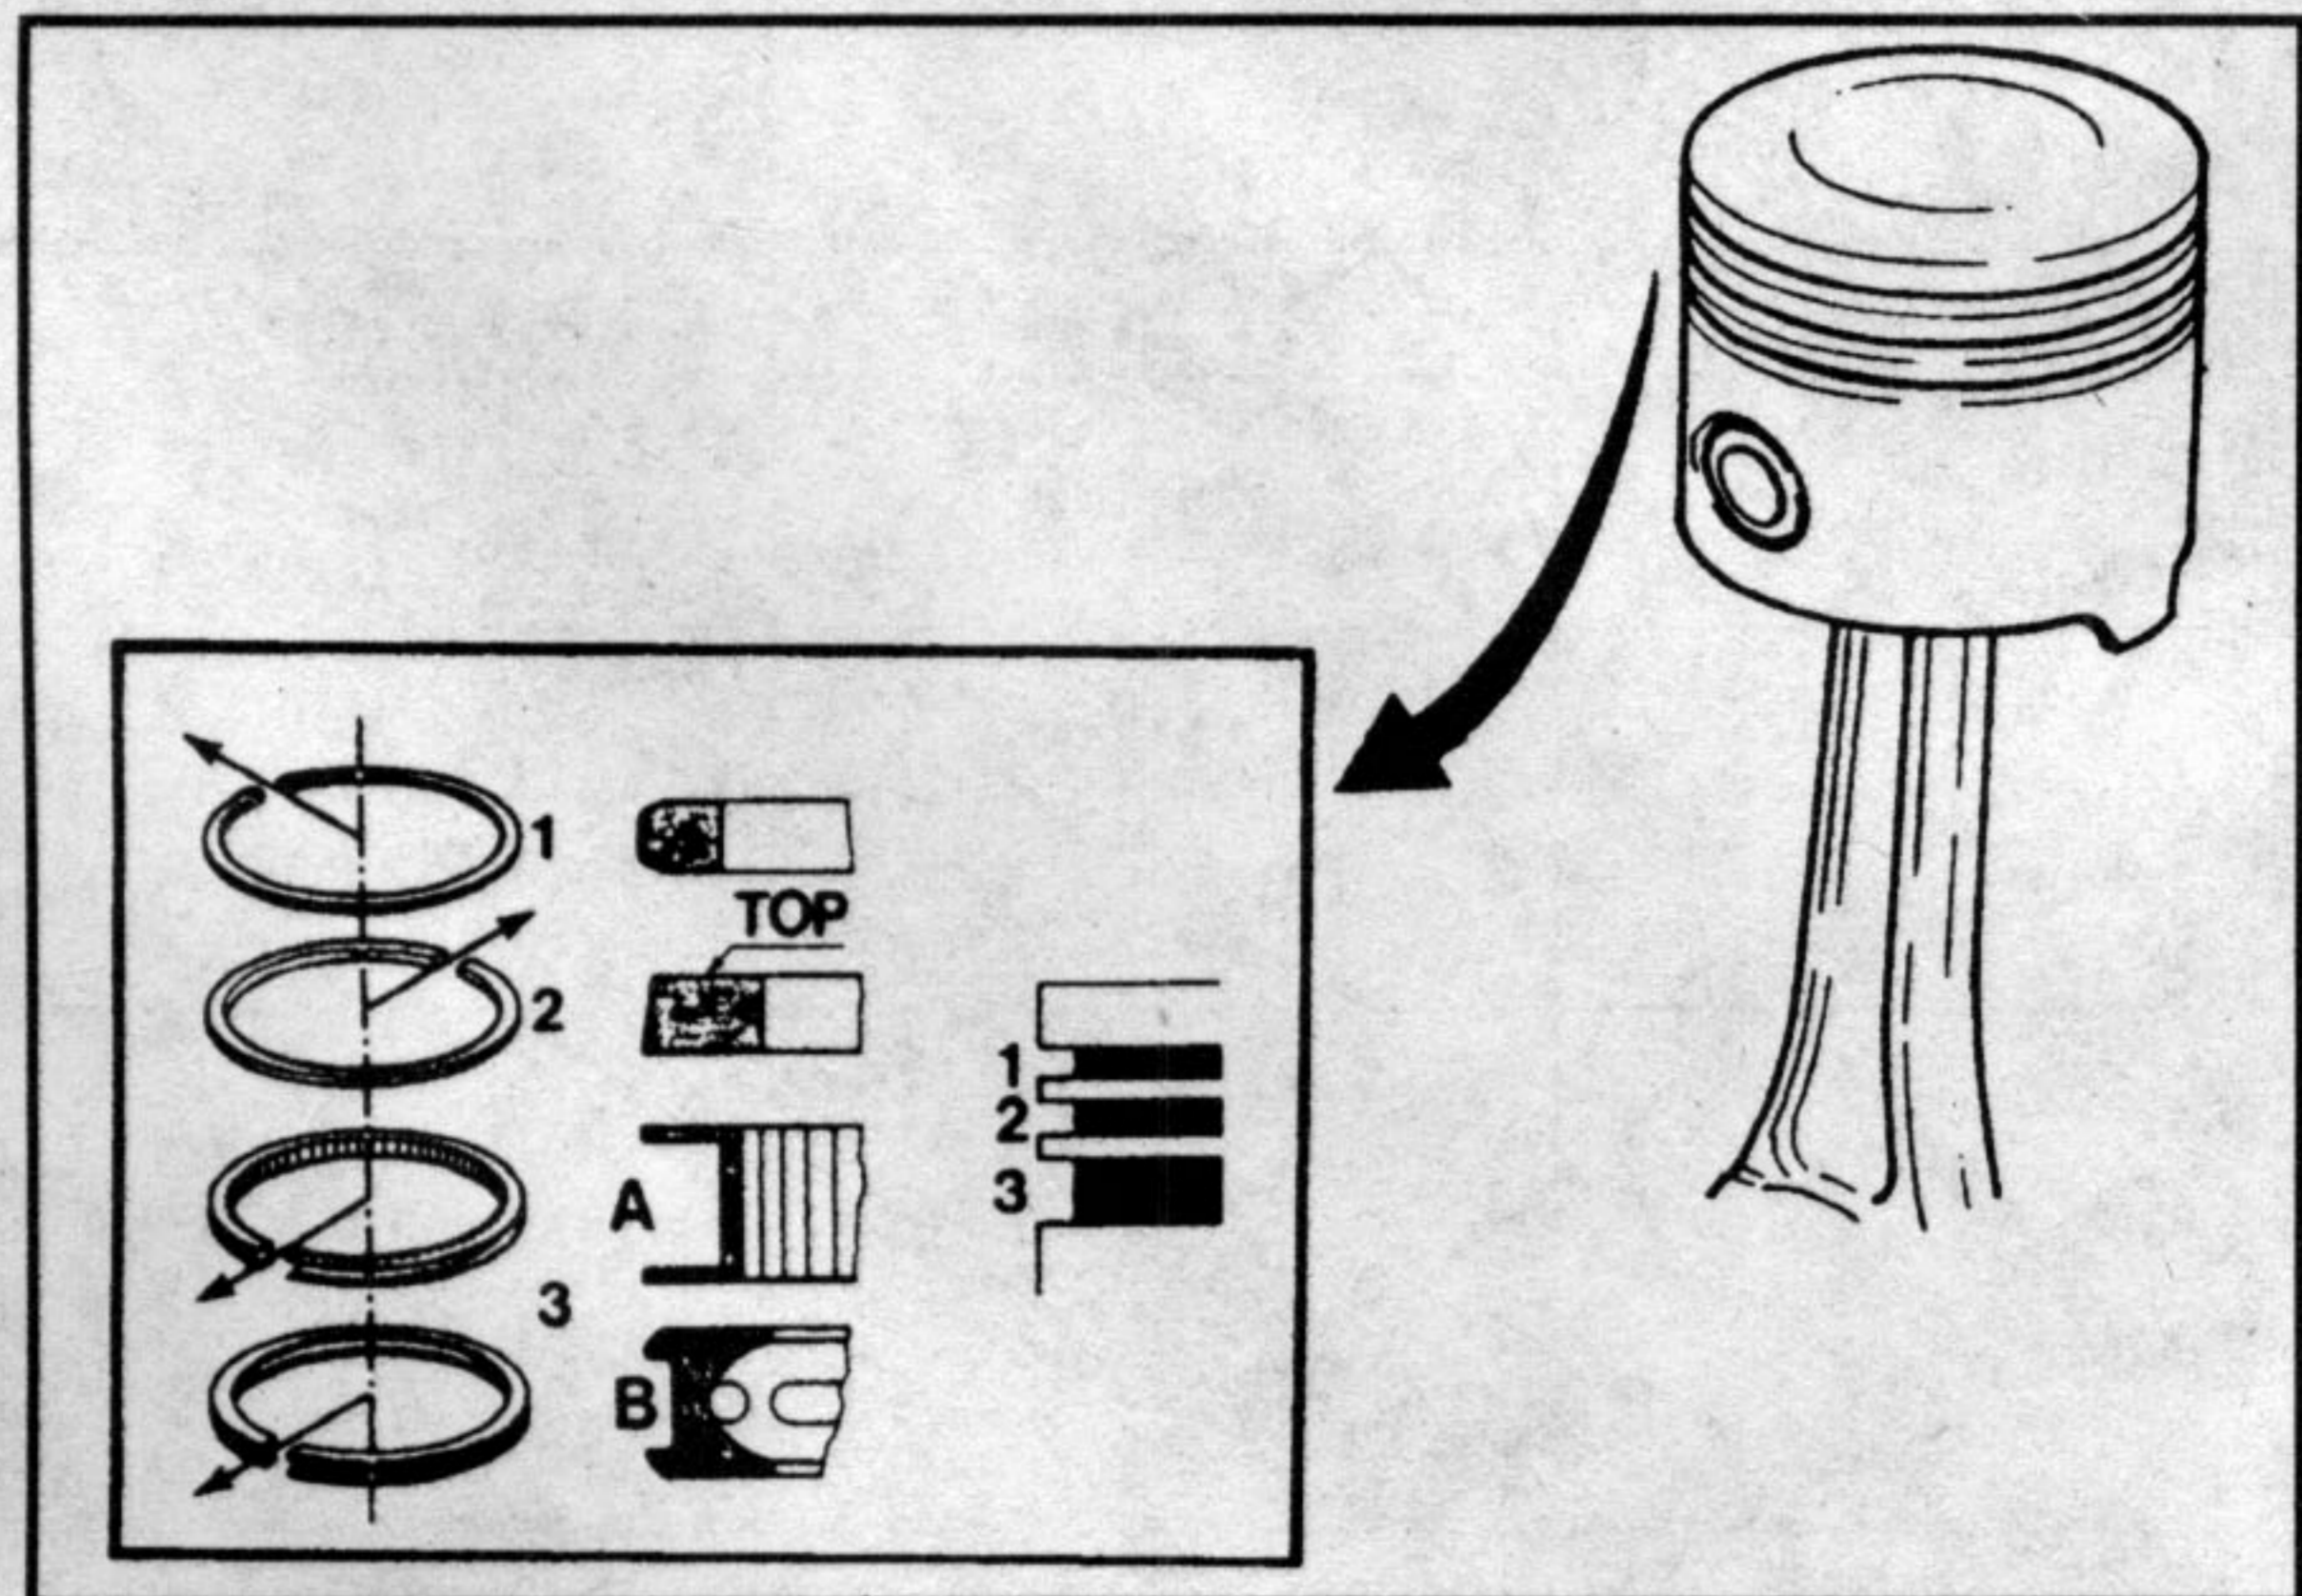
Двигатель В13/В14. Расположение и профиль поршневых колец
